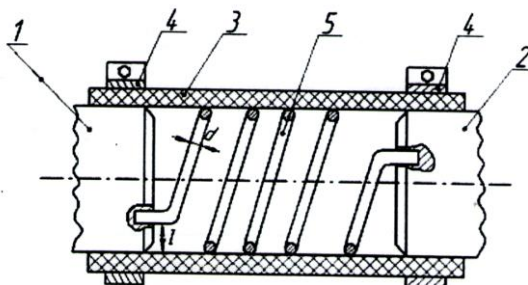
Модернизированная муфта для соединения валов. 1, 2 - валы, 3 – гибкая цилиндрическая деталь, 4 – элемент для закрепления гибкой цилиндрической детали, 5 – пружина сжатия
